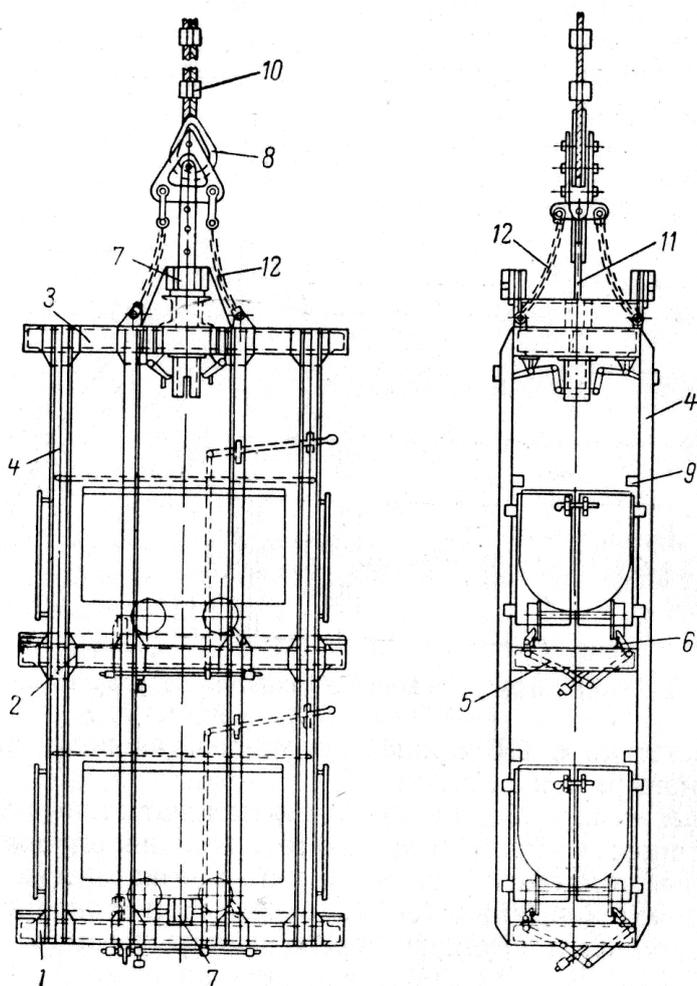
Двухэтажная клеть для деревянных проводников: 1 – нижний пояс клетки; 2 – средний пояс; 3 – верхний пояс; 4 – вертикальные стойки; 5 – площадки клетки; 6 – рельсовый путь; 7 – направляющие лапы; 8 – коуш; 9 – поручни; 10 – жимки; 11 – стяжной несущий болт; 12 – предохранительные цепи
